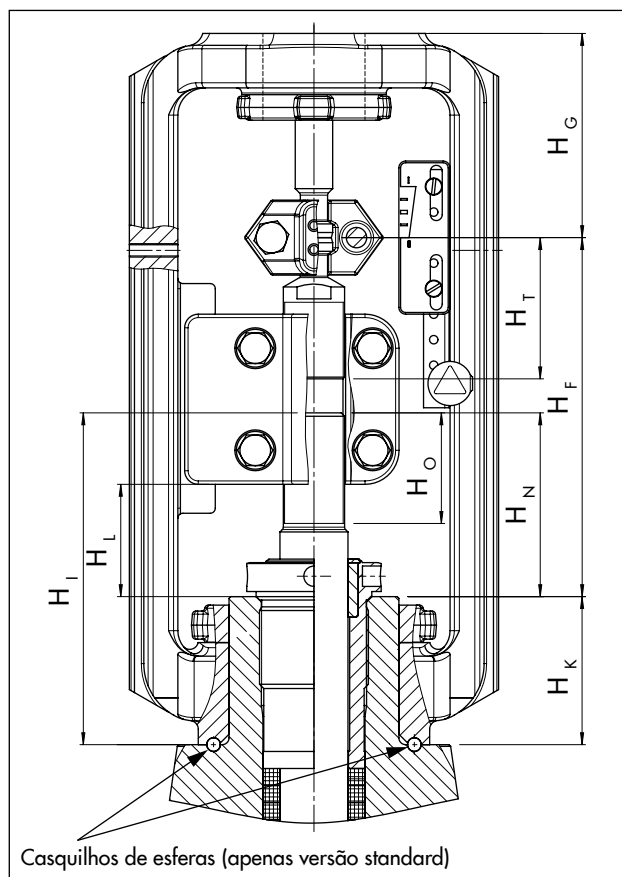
Desenho cotado com dimensões de montagem para atuadores pneumáticos Tipos 3271 e 3277
